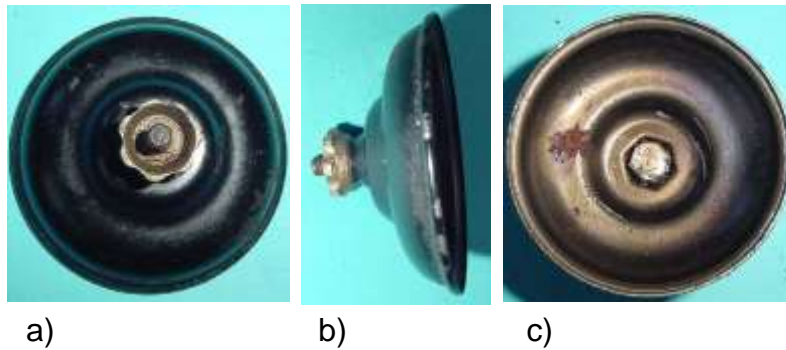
Stahlboden mit Kabelanschlussbolzen
